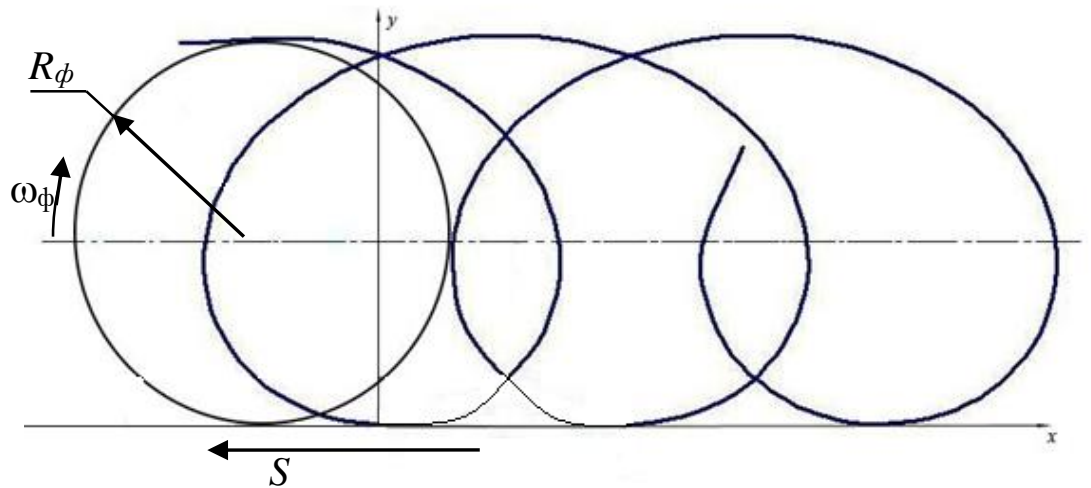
Траєкторія руху фрези при зустрічному фрезеруванні
